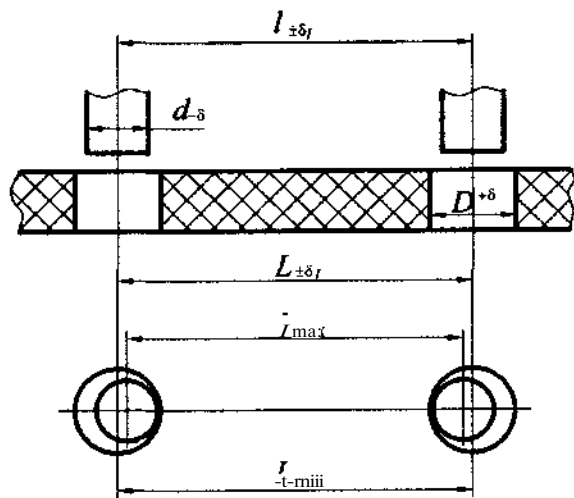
Схема сборки деталей, сопрягаемых по двум цилиндрическим поверхностям
